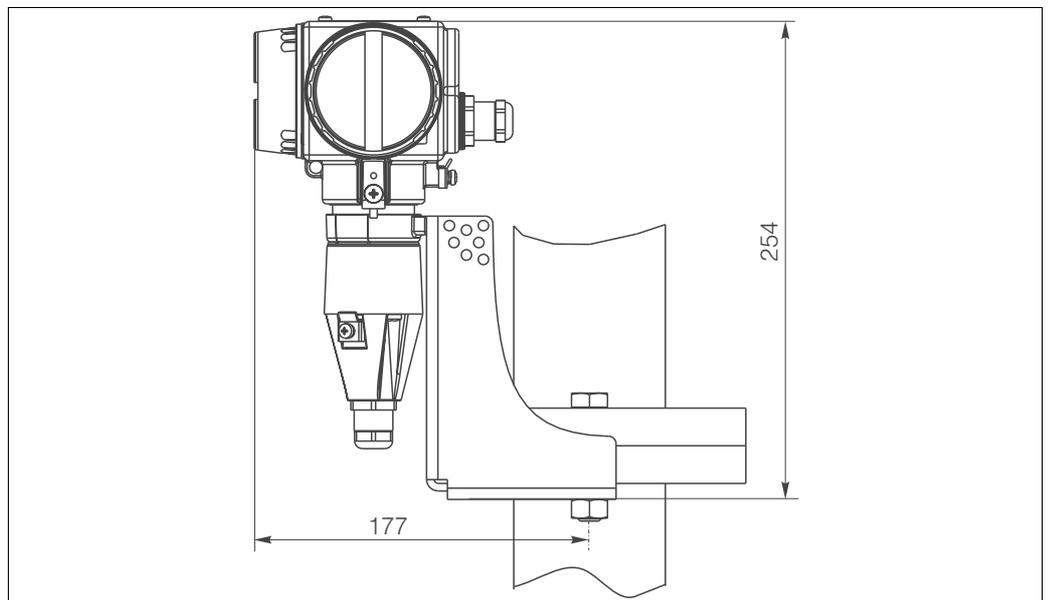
CLM 431: Flanschmontage m. Befestigungswinkel (bei CLM431-xxx4xx im Lieferumfang)
